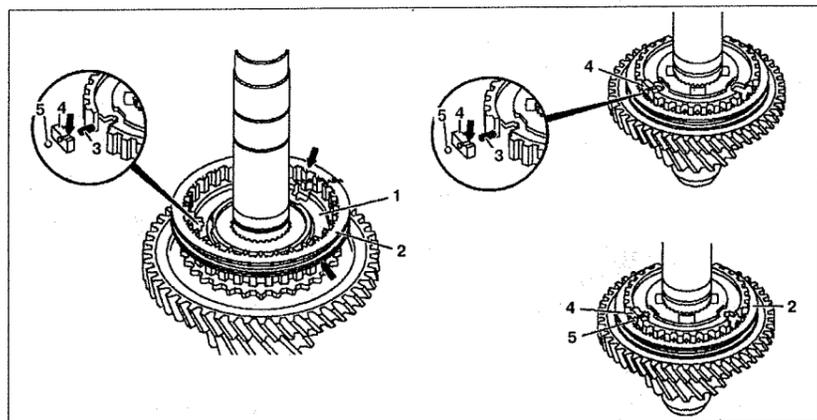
Разборка и сборка муфты синхронизатора включения 1-й и 2-й передач (автомобили с двигателями 111.948 и 601.970):
